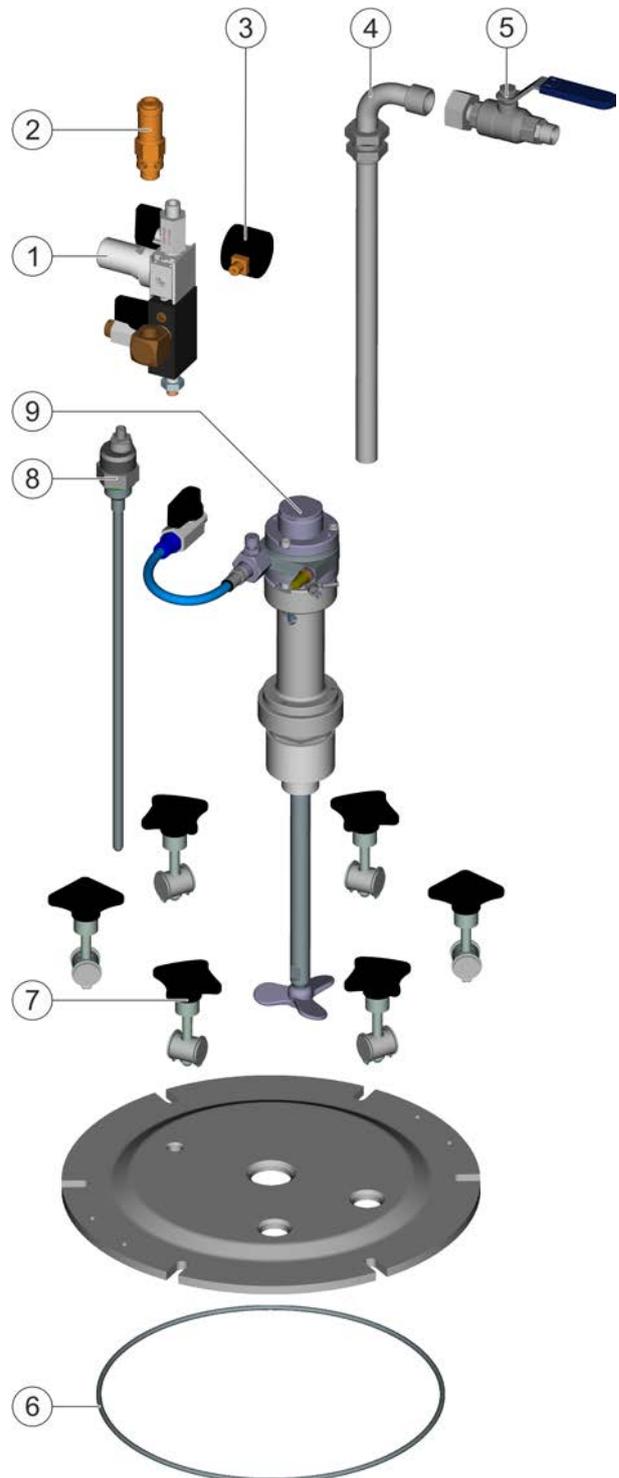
Couvercle (exemple pour les variantes 1 et 2)
